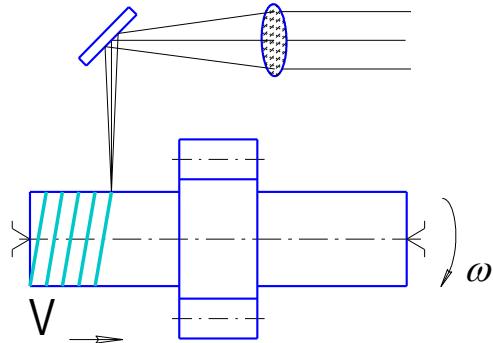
Схема восстановления шестерен насосов НШ лазерной наваркой металлических порошков
